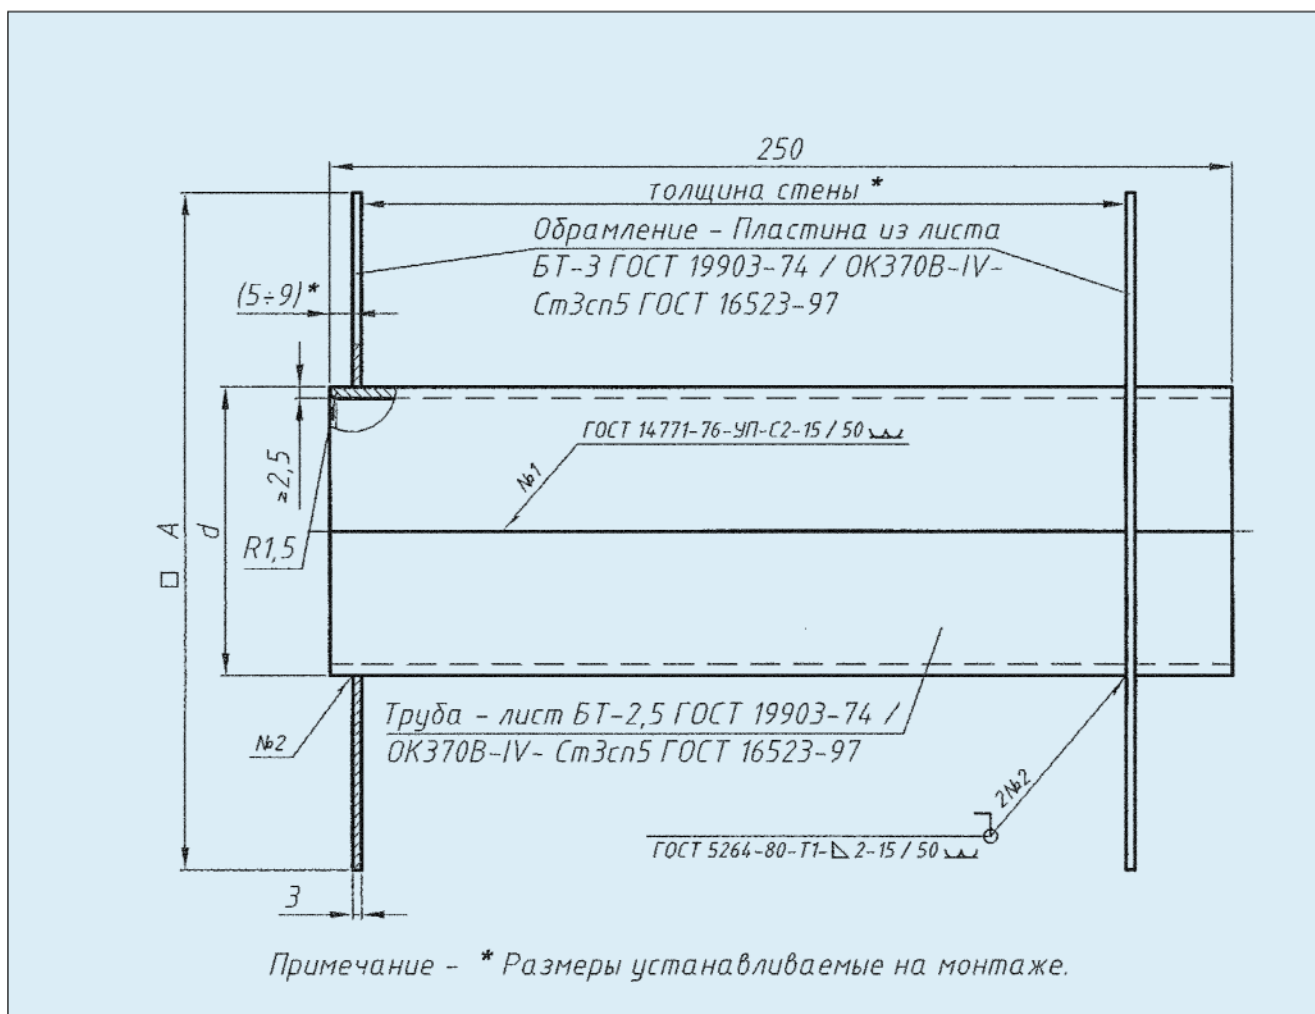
Общий вид проходок трубчатых (их металлоконструкций).
